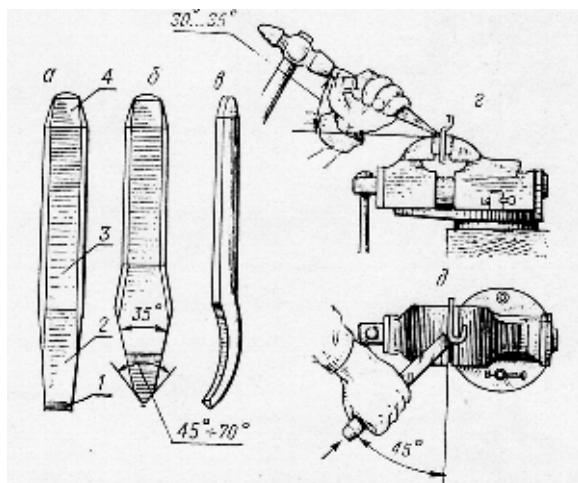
Инструменты для рубки и углы наклона зубила по отношению к оси губок тисков и обрабатываемой поверхности заготовки
